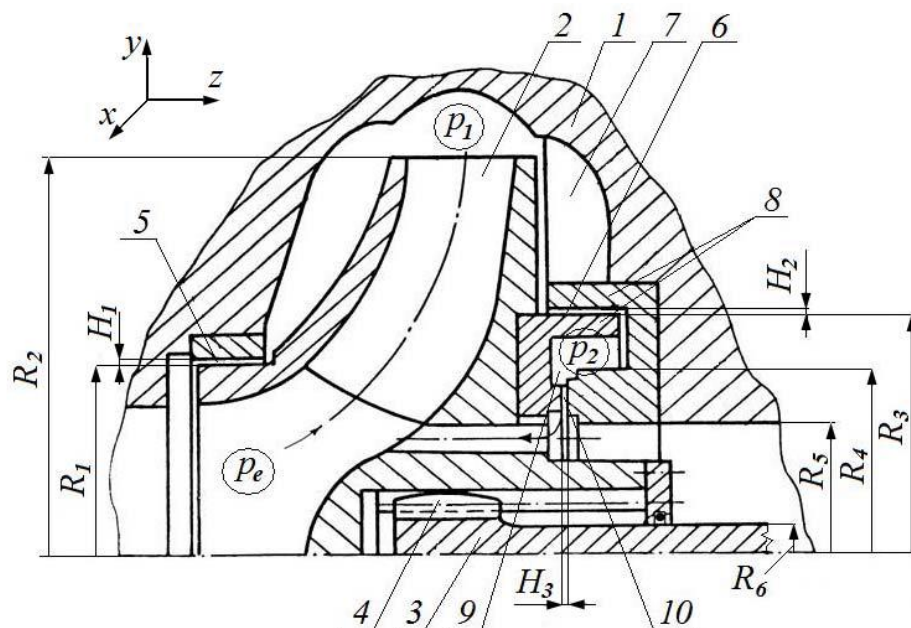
Геометрія робочого колеса з розвантажувальним пристроєм
